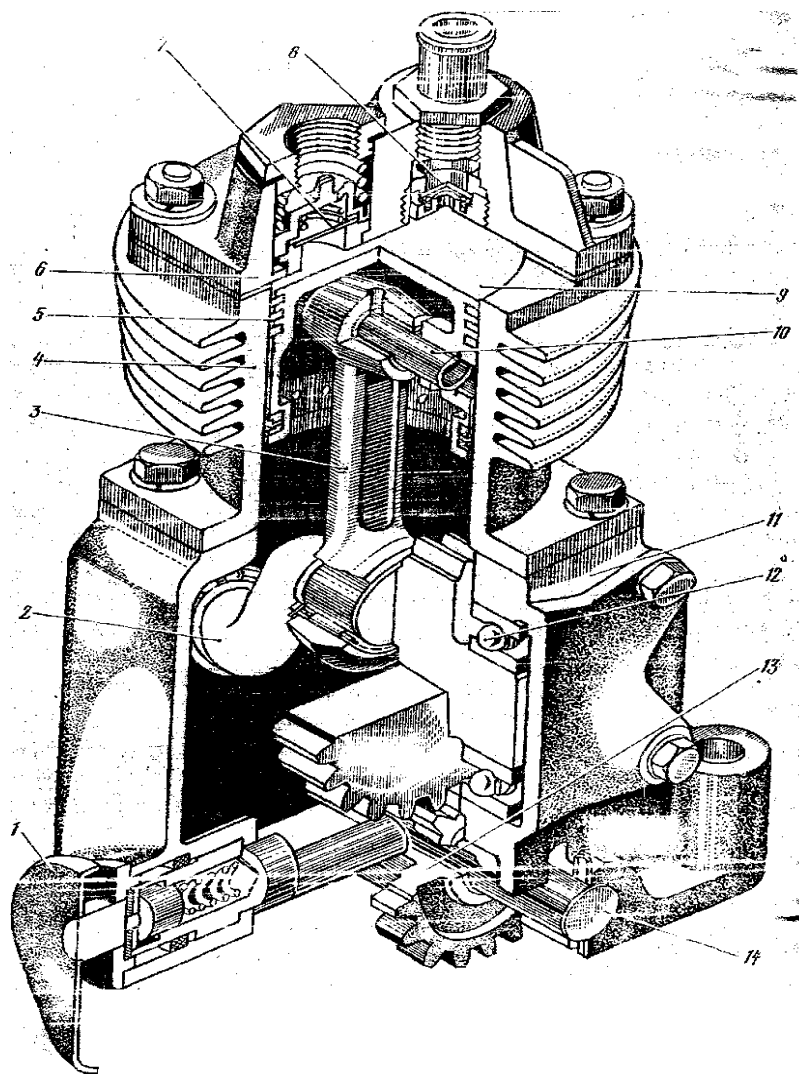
Компрессор: 1 – рукоятка включения привода; 2 – коленчатый вал; 3 – шатун; 4 – цилиндр; 5 – поршневые кольца; 6 – головка цилиндров; 7 – нагнетательный клапан; 8 – всасывающий клапан; 9 – поршень; 10 – поршневой палец; 11 – картер; 12 – подшипник коленвала; 13 – промежуточная шестерня; 14 – шестерни
